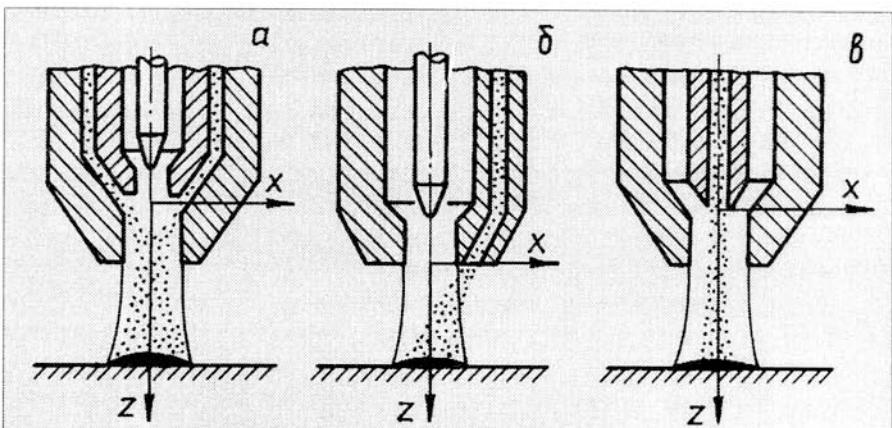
Схемы ввода порошка в дугу при плазменно-порошковой наплавке
